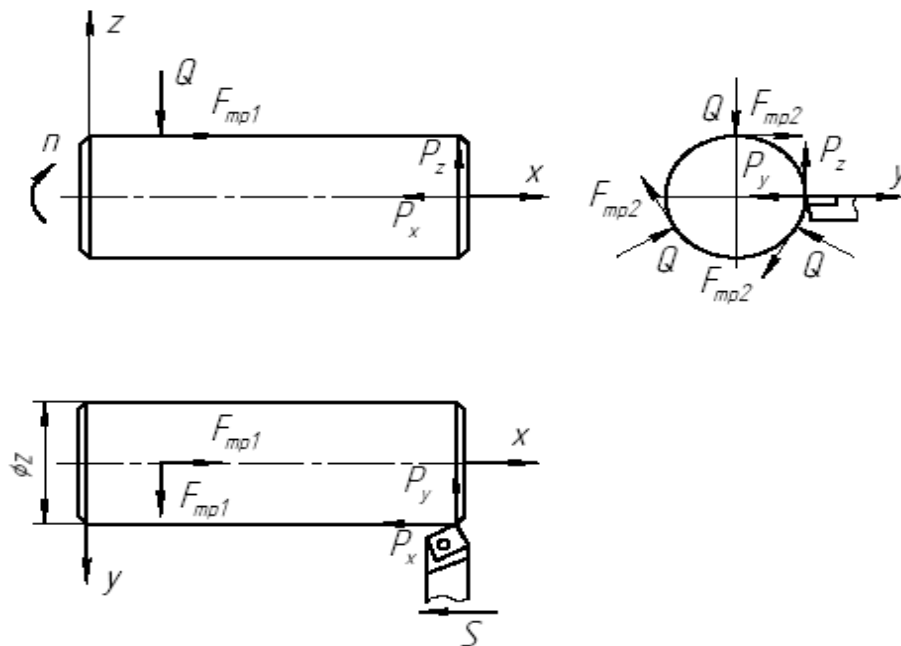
Схема сил, що діють на заготовку в процесі обробки
